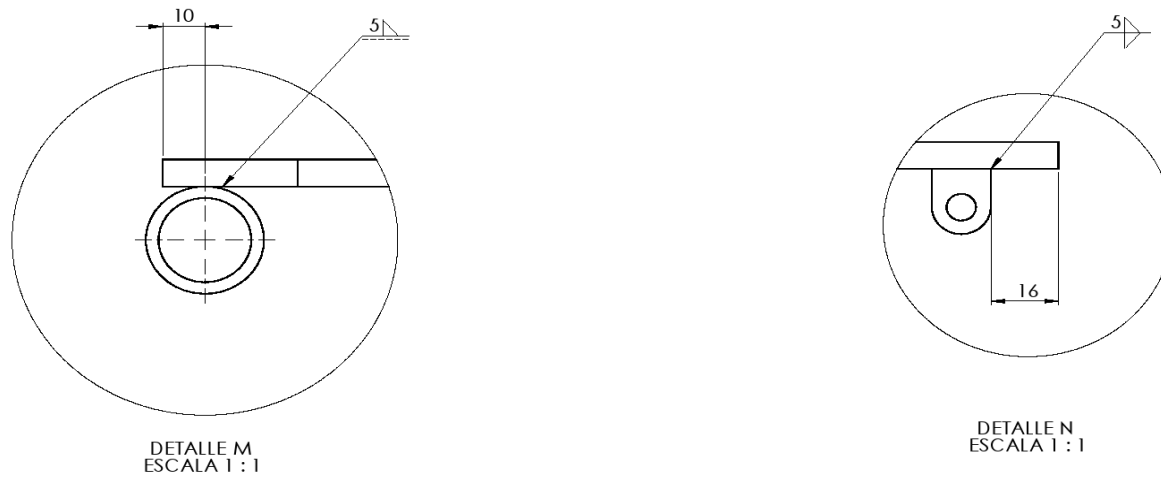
Vista de detalles M y N del ensamble de la rampa. Fuente: Elaboración propia.
